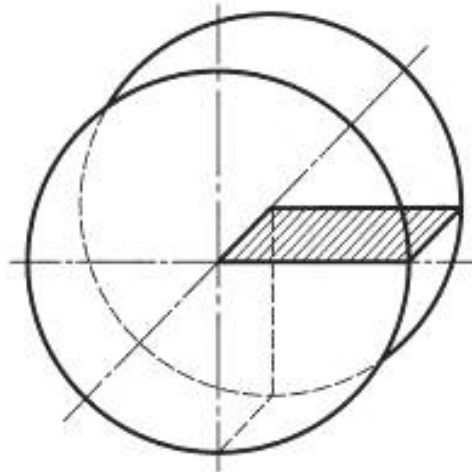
Образец от прутка или заготовки с диаметром или длиной стороны свыше 25 до 40 мм включительно
